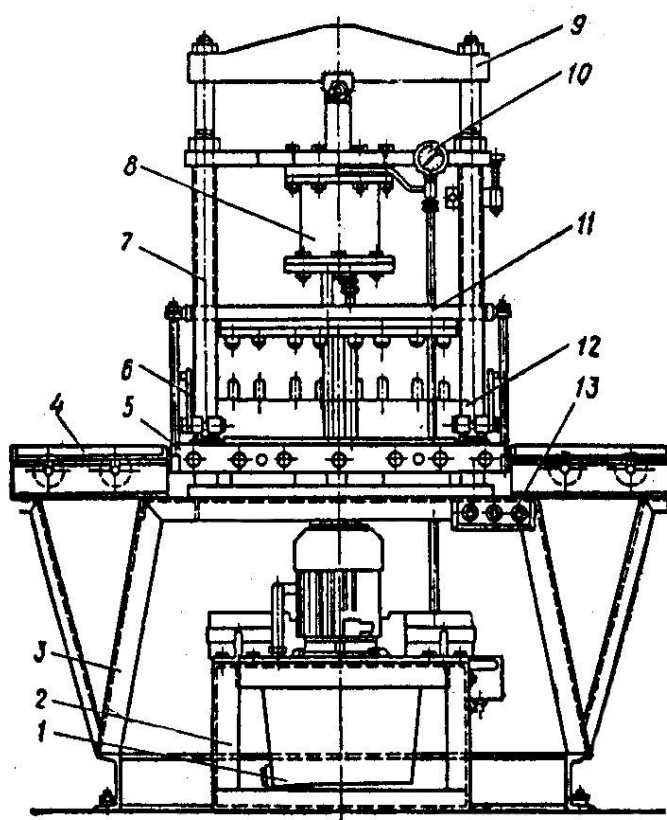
Специальный пресс для запрессовки и выпрессовки направляющих втулок клапанов головки цилиндров:
